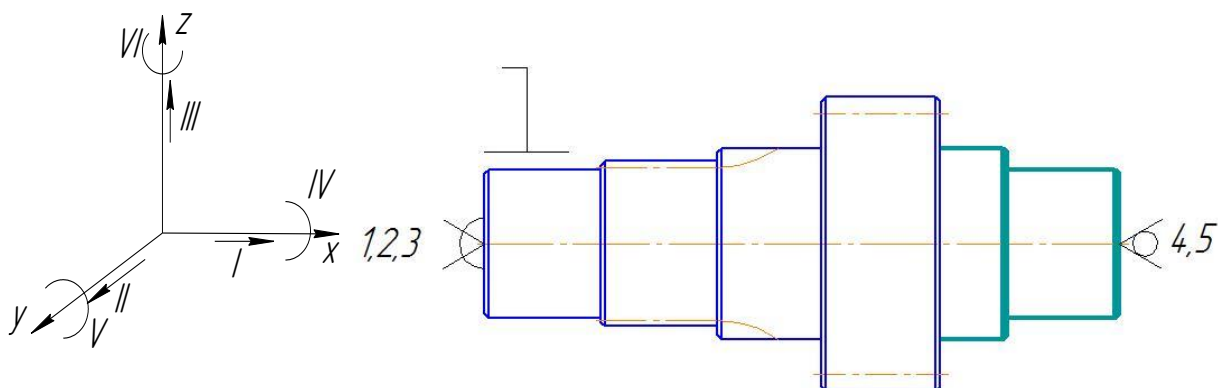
Ескіз обробки заготовки на операції 050
